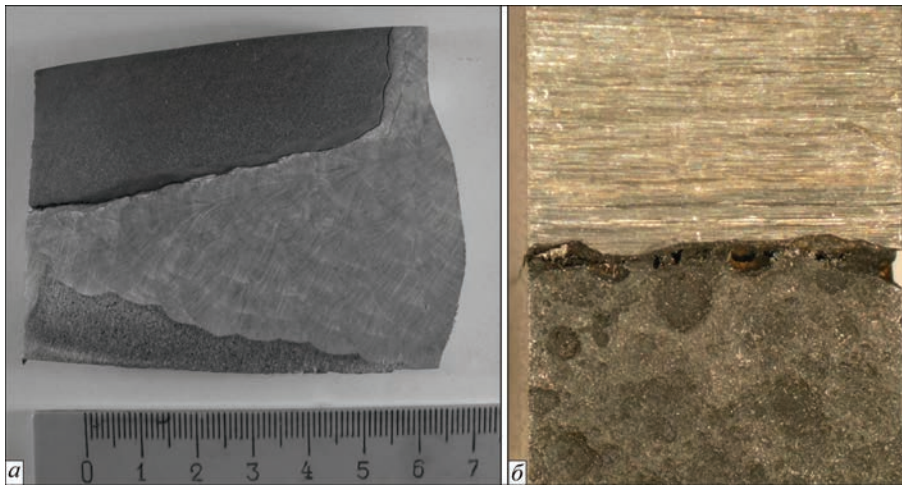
Макроструктура зразка зварного з'єднання: *a* — вид в поперечному перерізі; *б* — вид на внутрішню поверхню, яка контактує з робочим середовищем 2-го контуру [7]
